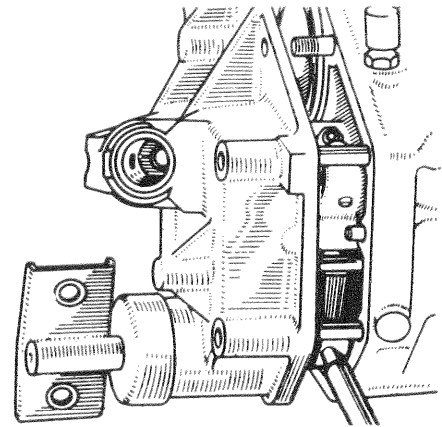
Présentation du couvercle de tachymètre et goupillage du doigt sur son axe
